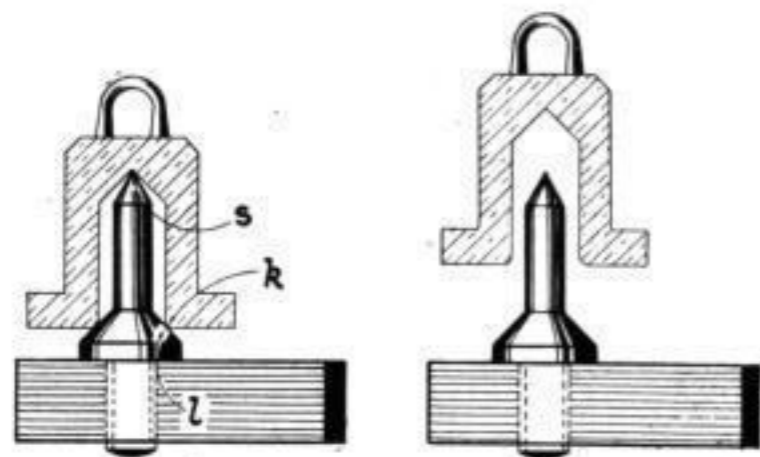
Das glockenförmige Gewicht: aufgesetzt und abgehoben
